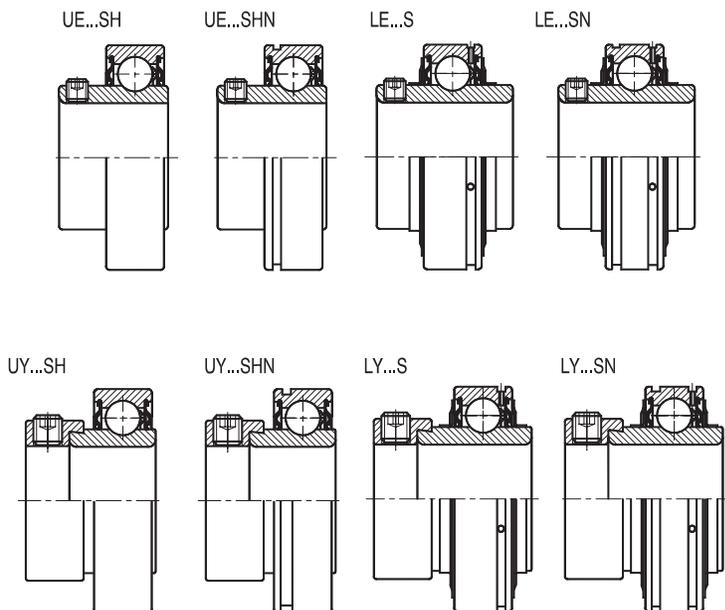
Подобные подшипники – цилиндрические – наружный вид
